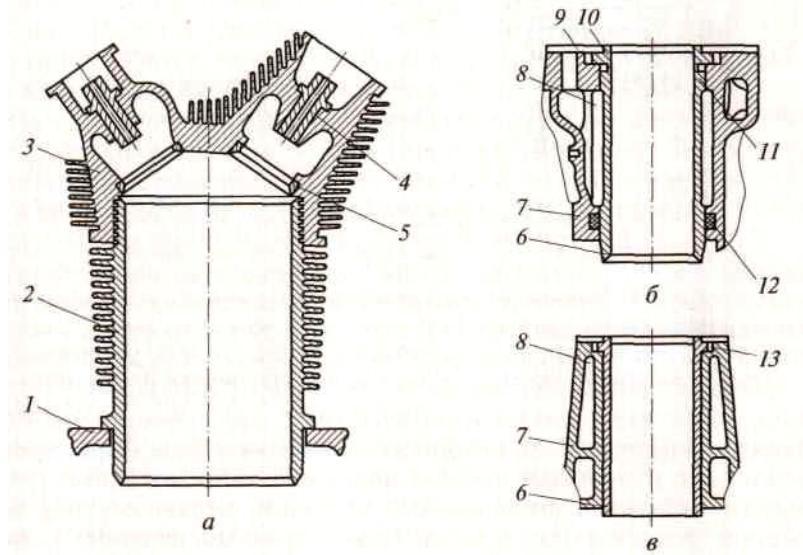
Цилиндр и гильзы цилиндров двигателя:
